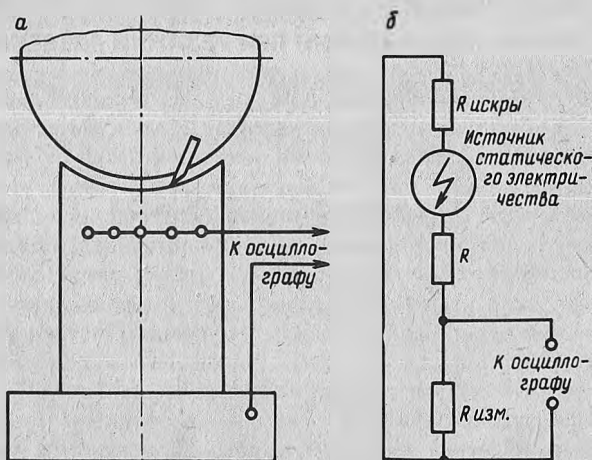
Схема замера напряжения на образце (а): 1 — фреза; 2 — образец; 3 — ряд контактов; 4 — губки тисков, в которые зажимался образец; б — эквивалентная электрическая схема измерения потенциала.
